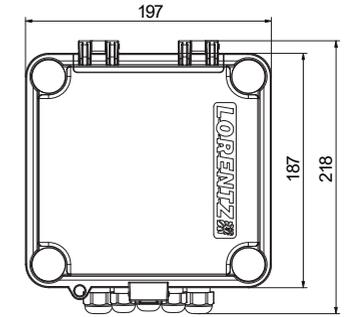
PV Disconnect 400-50-1-S (Vue de dessous):
